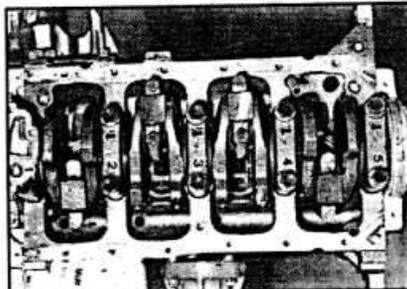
Е.35. Нумерация и расположение крышек коренных подшипников (стрелки направлены в сторону привода газораспределения).
